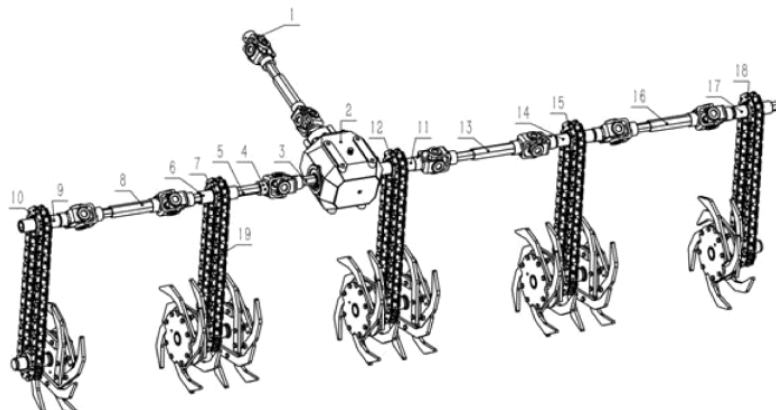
Схема почвообрабатывающей фрезы для обработки посадок картофеля.
